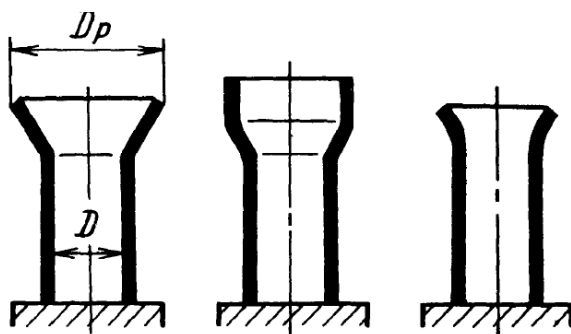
Детали, получаемые раздачей краевой части заготовки
